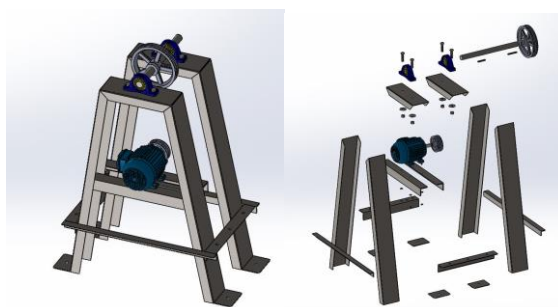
Diseño Paramétrico Soporte Motorizado del Mandril
